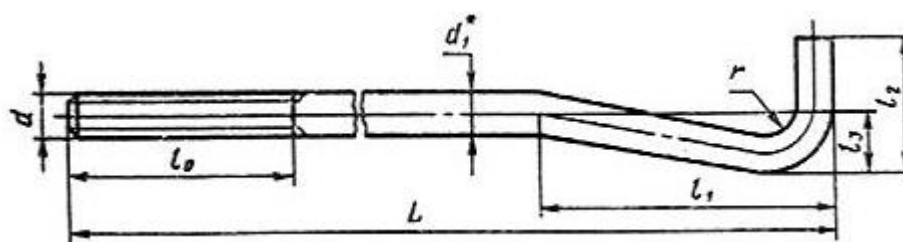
Расчетная схема изогнутого фундаментного болта
